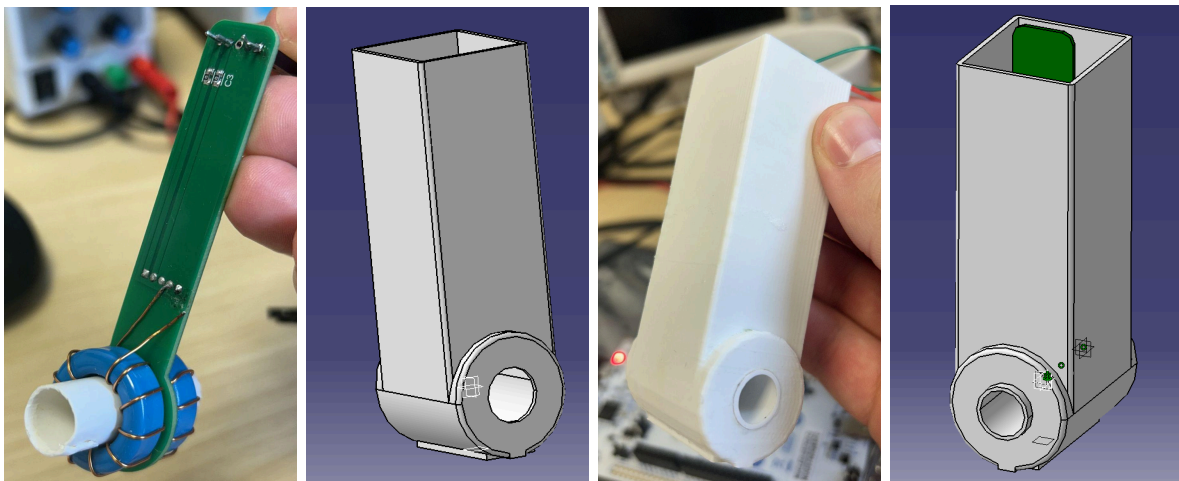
TEST BOBINE ET COQUE CAPTEUR
